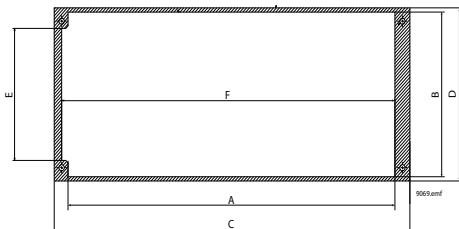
Dimensões do recorte para montagem com flange do MR4 ao MR6
